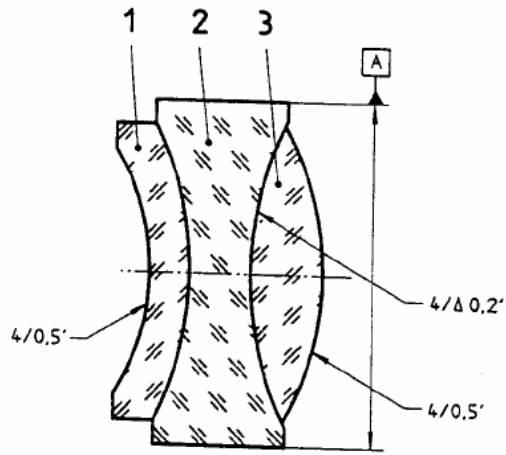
Складальний вузол, що включає позначення допуску на клейовий клин, а базова вісь визначається зовнішнім циліндром
